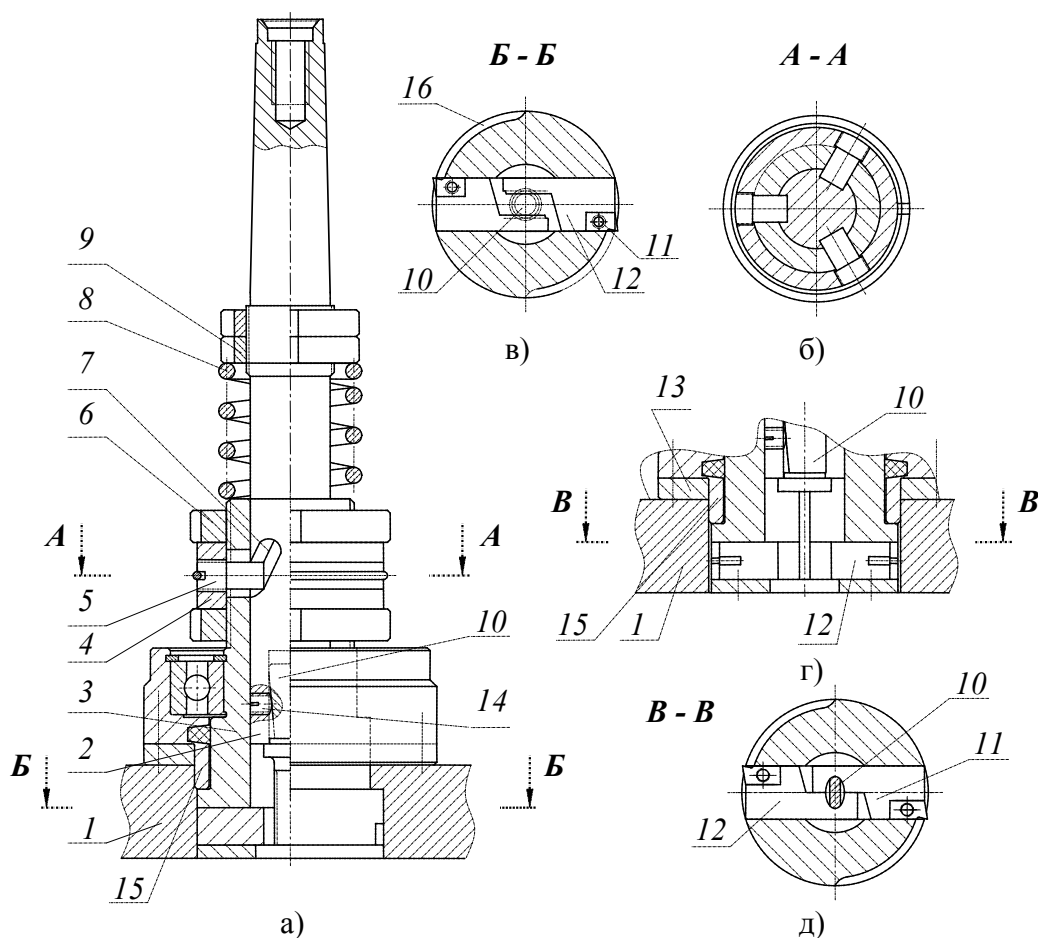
Пристрій для розточування кільцевих канавок в отворах корпусних деталей з використанням кінематичних зв'язків оправка-різець з'єднань:
